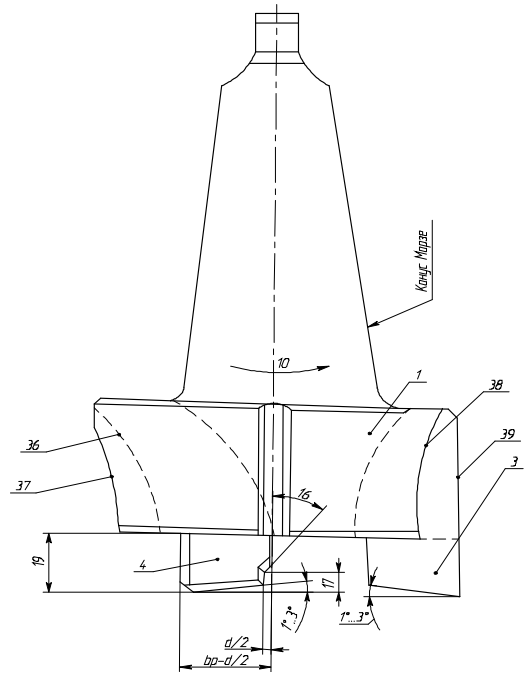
Исполнение 7 резцовой головки с наклоном главных режущих кромок внутрь.
